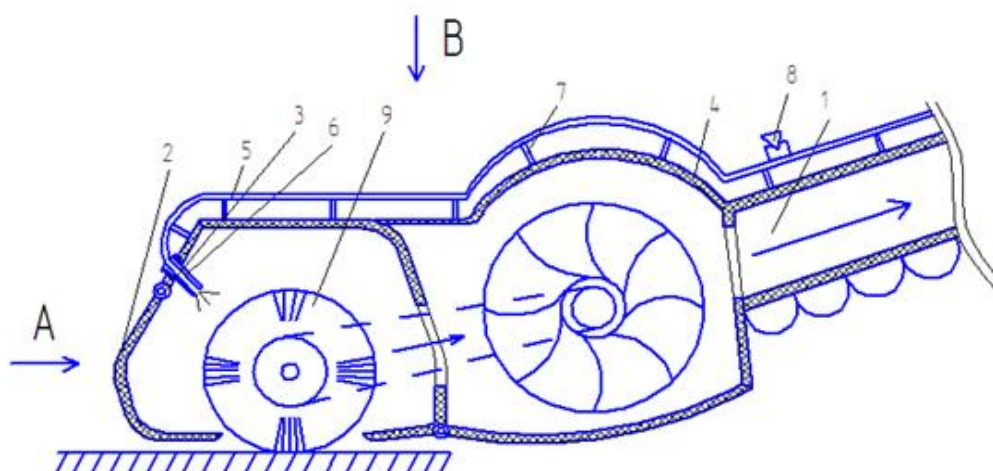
Устройство для очистки кожного покрова КРС. Поперечный разрез.
